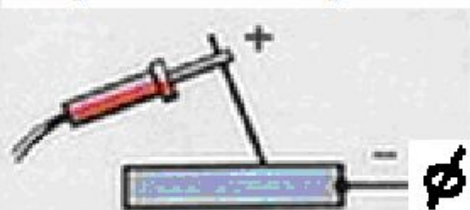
С Схема сварки на постоянном токе обратной полярности
